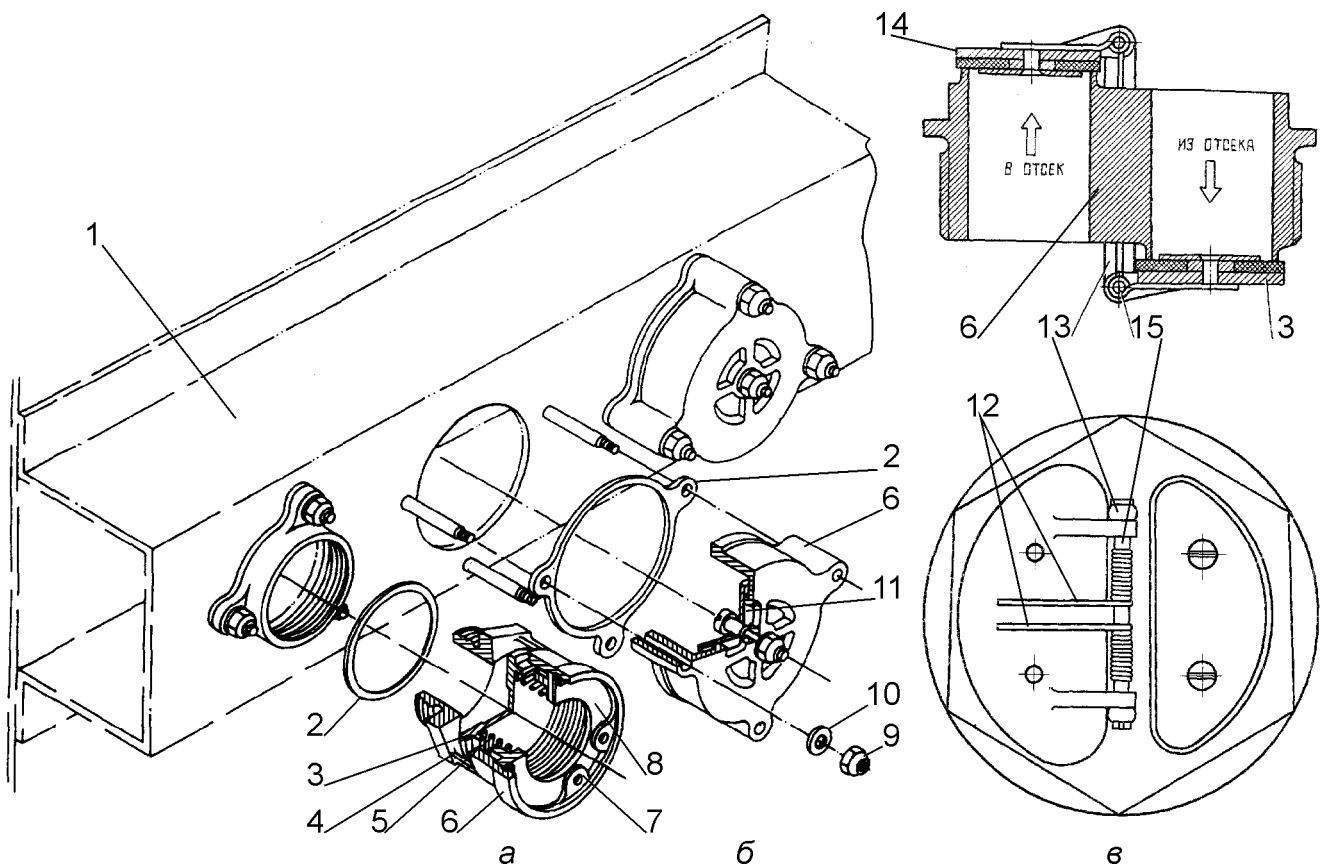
Клапани: а — запобіжний (Ил-96); б — вакуумний (Ил-96); в — комбінований (Як-40); 1 — дренажний стрингер; 2 — прокладки; 3 — тарілки запобіжних клапанів; 4 — вікно в корпусі; 5 — пружина стискання; 6 — корпуси клапанів; 7 — стопорне кільце; 8 — втулка; 9 — гайка; 10 — шайба; 11 — пружинний клапан; 12 — пружини кручення; 13 — стояк; 14 — тарілка вакуум-клапана; 15 — осі
